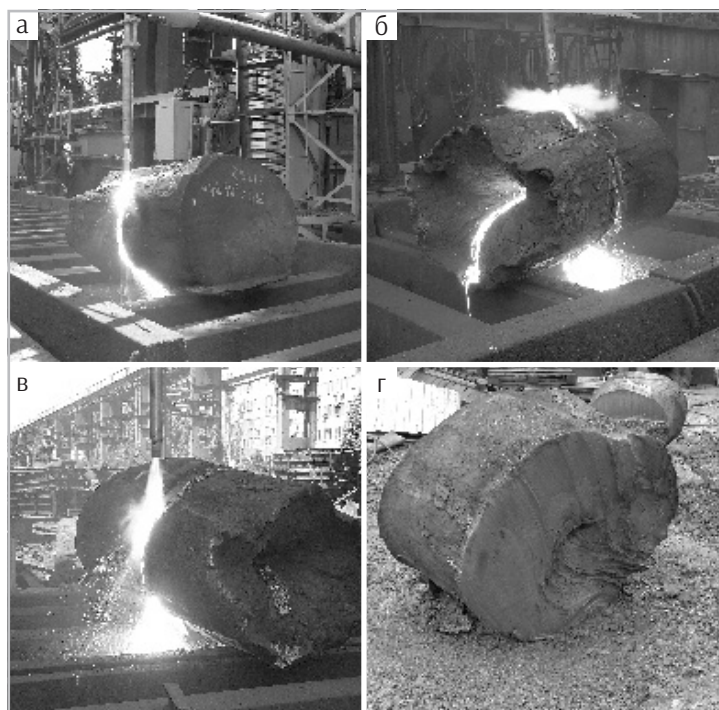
Резка конца поковки Ø 1000 мм с усадочной раковиной: а — начало; б — середина резки; в — окончание резки; г — поверхность реза
